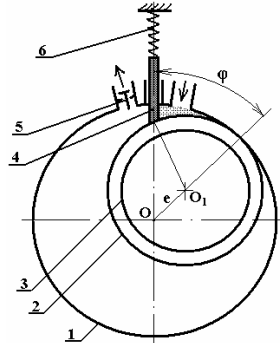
Схема ротаційного компресора з ротором, що перекочується
